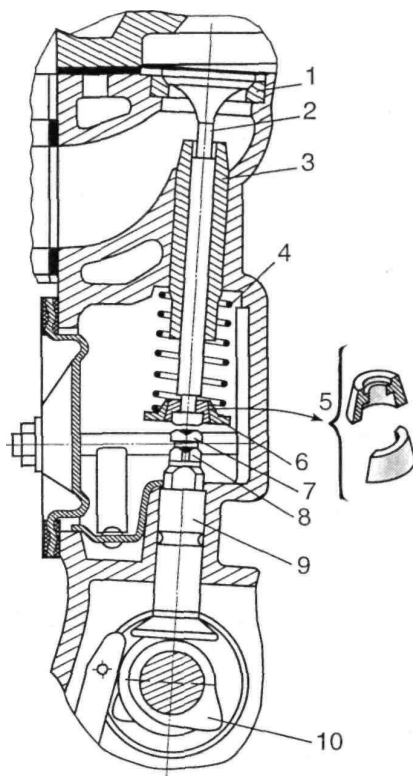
Механізм газорозподілу двигунів з нижнім розташуванням розподільного вала та клапанів:
